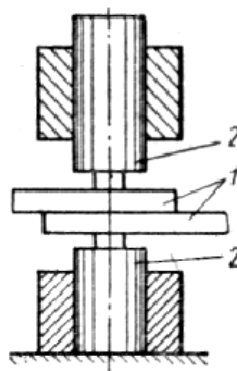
Схема сварки без предварительного зажатия свариваемых деталей: 1 – свариваемые детали, 2 – пуансоны.
